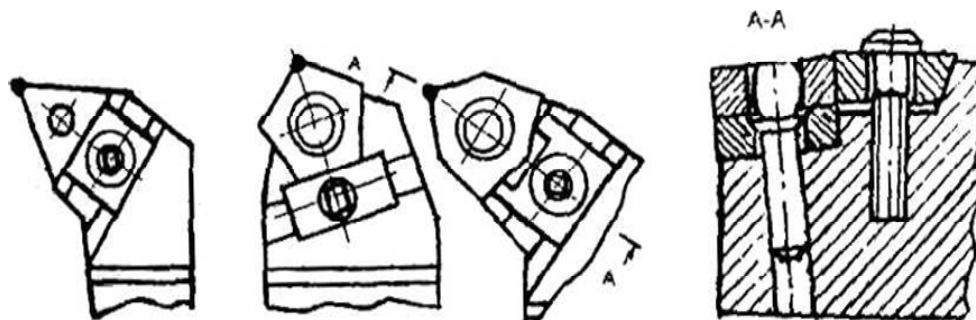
Эскизы рабочей части сборных инструментов: тип крепления РТ
